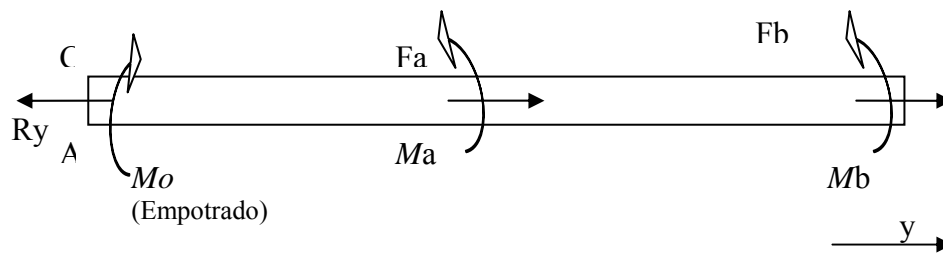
32. Diagrama de cuerpo libre de la Columna de la Prensa colocada en posición horizontal para su estudio. Fuente: Los Autores.
